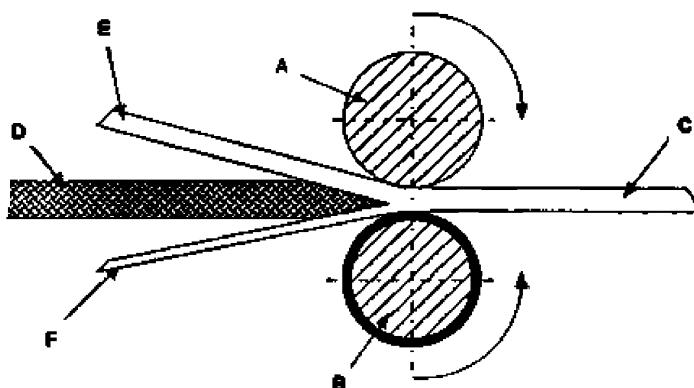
Принцип работы типичного механизма по подготовке испытательных образцов
